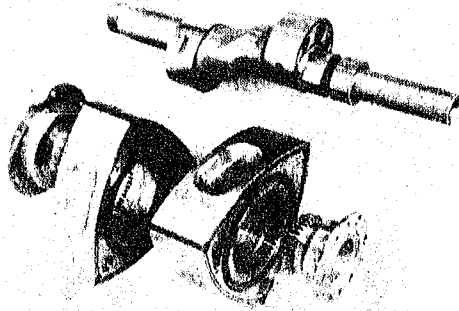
Läufer, Phasengetriebe und Excenterwelle
